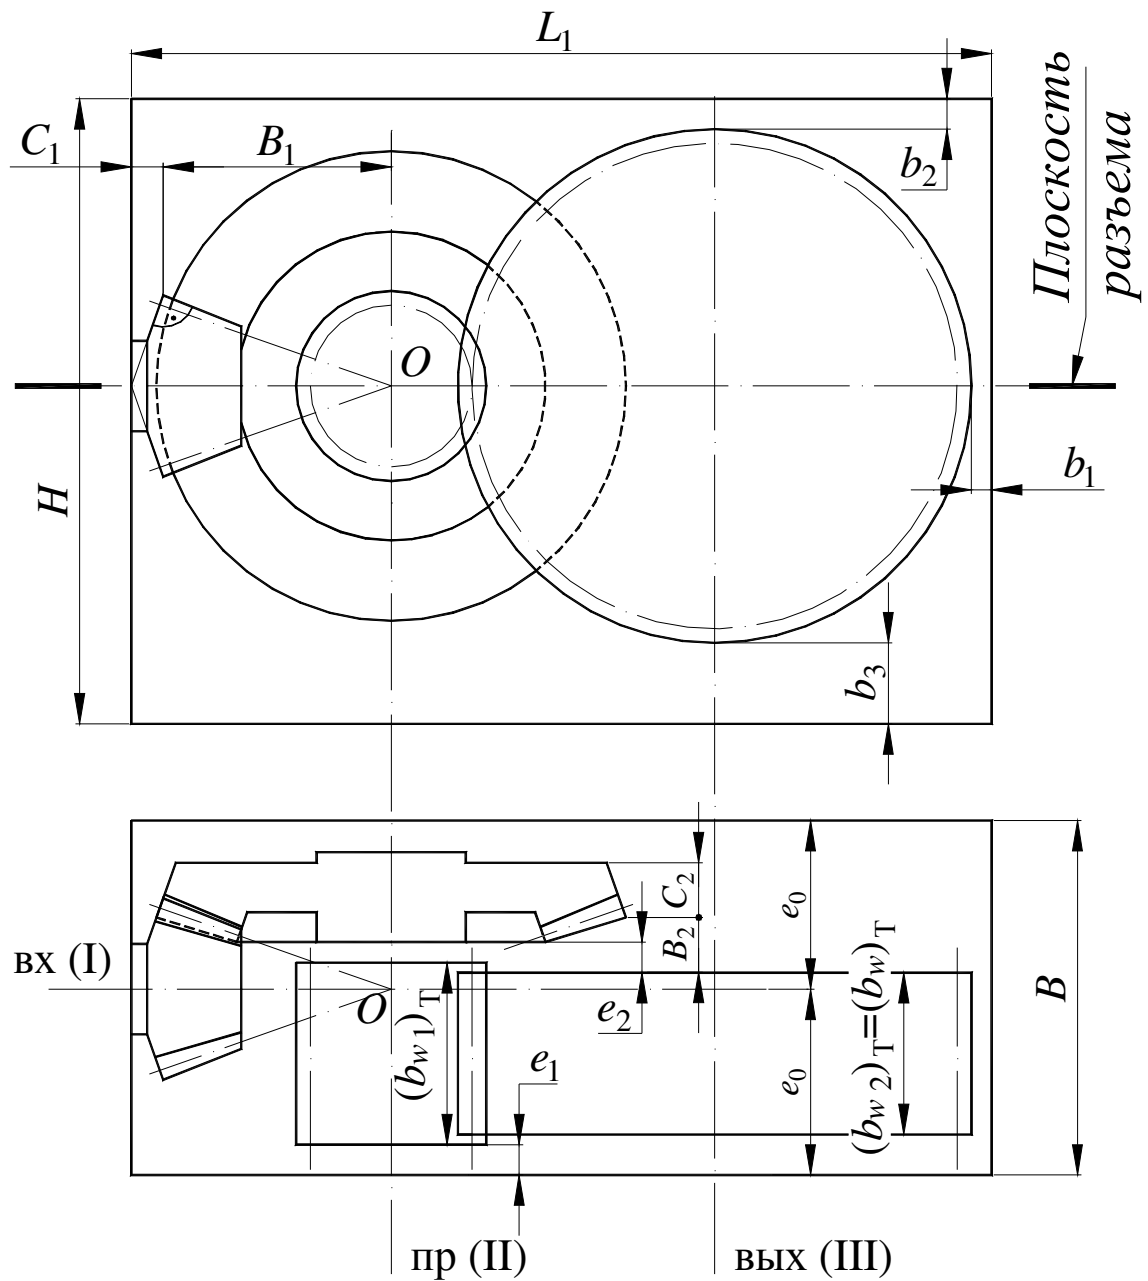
Второй этап эскизной компоновки коническо-цилиндрического редуктора
